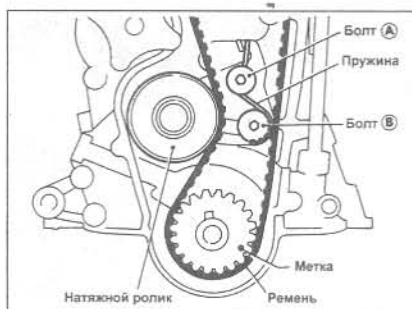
Детали механизма натяжения зубчатого ремня привода (Глава 5)
